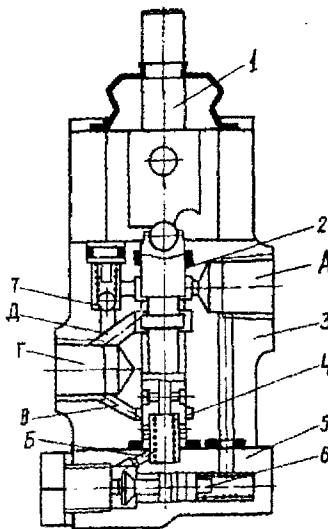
Распределитель блокировки дифференциала заднего моста тракторов семейства МТЗ: 1 - рычаг; 2 - золотник; 3 - корпус; 4 - пружина; 5 - крышка; 6 - редукционный клапан; 7 - предохранительный клапан; А - сливная магистраль; Б - магистраль клапана блокировки; Г - полость, соединенная с ГПМ блокировки; В и Д - подводящие каналы
